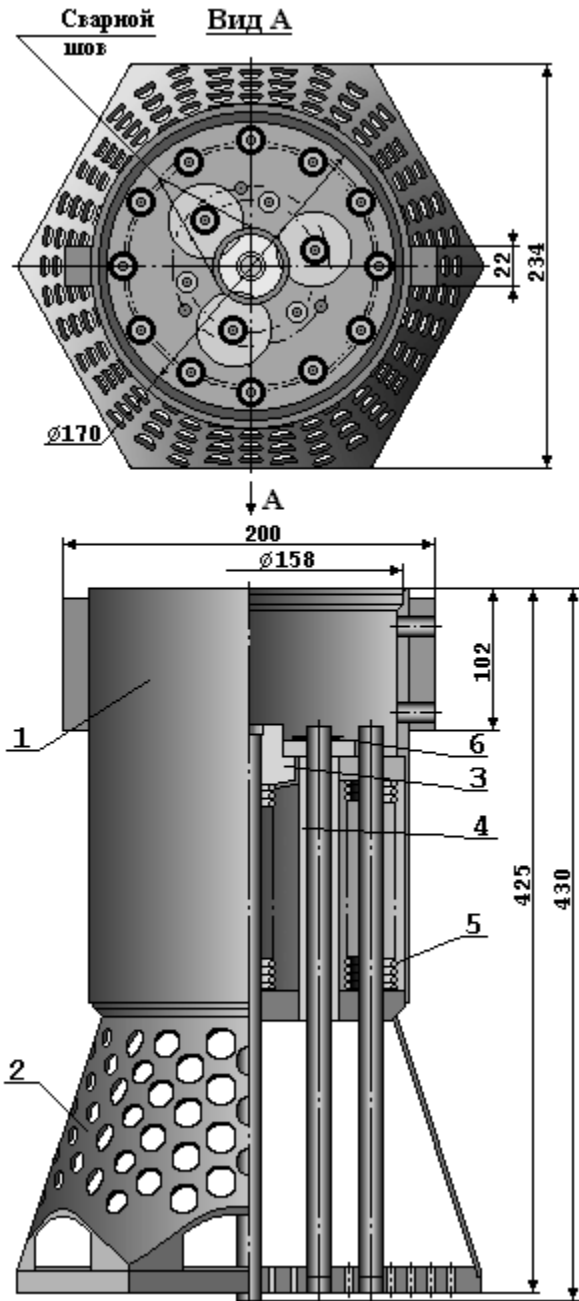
Головка базовой ТВС реактора ВВЭР-1000:
